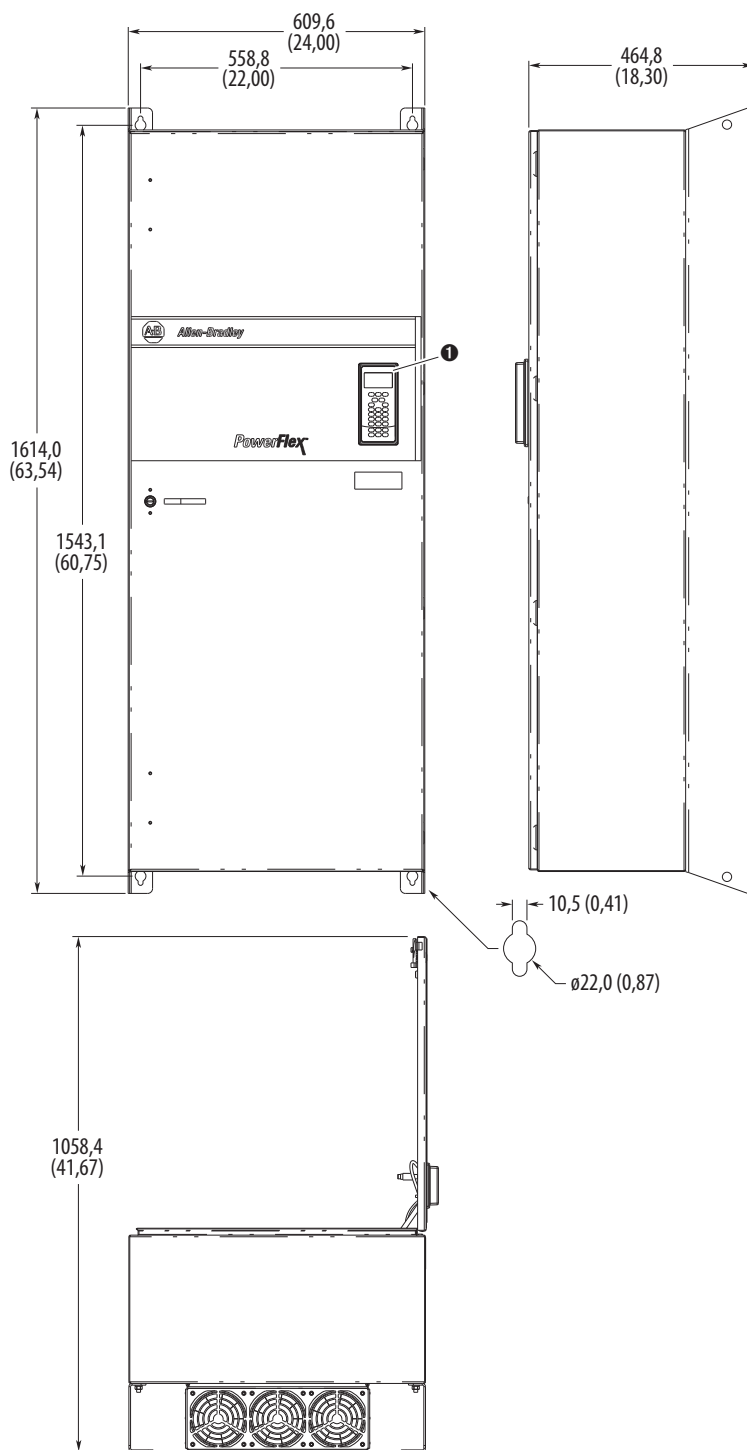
Комплект NEMA/UL тип 1, типоразмер 6
